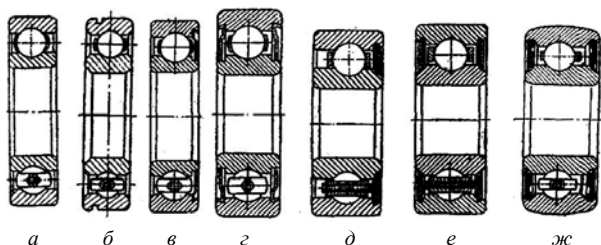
Шарикоподшипники радиальные однорядные типов:
